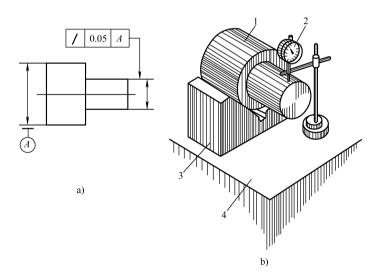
外圆表面径向圆跳动误差 a) 公差要求 b) 测量方法 1—被测零件 2—指示表 3—V 形架 4—平板
